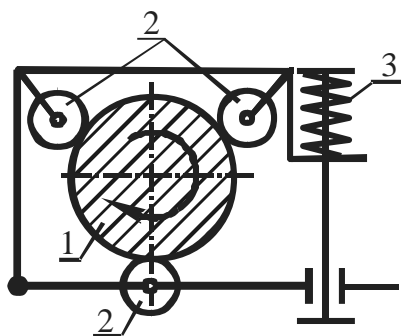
Схема обкатки деталей роликами: 1 – деталь, 2 – ролики, 3 – рабочая пружина
